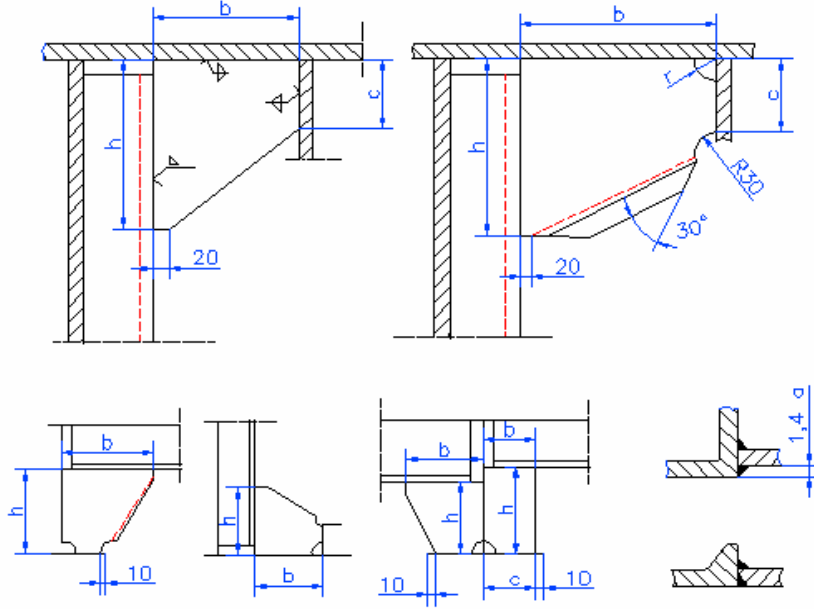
Kaplama sacının tank top sacı ile braketli birleştirmesi
